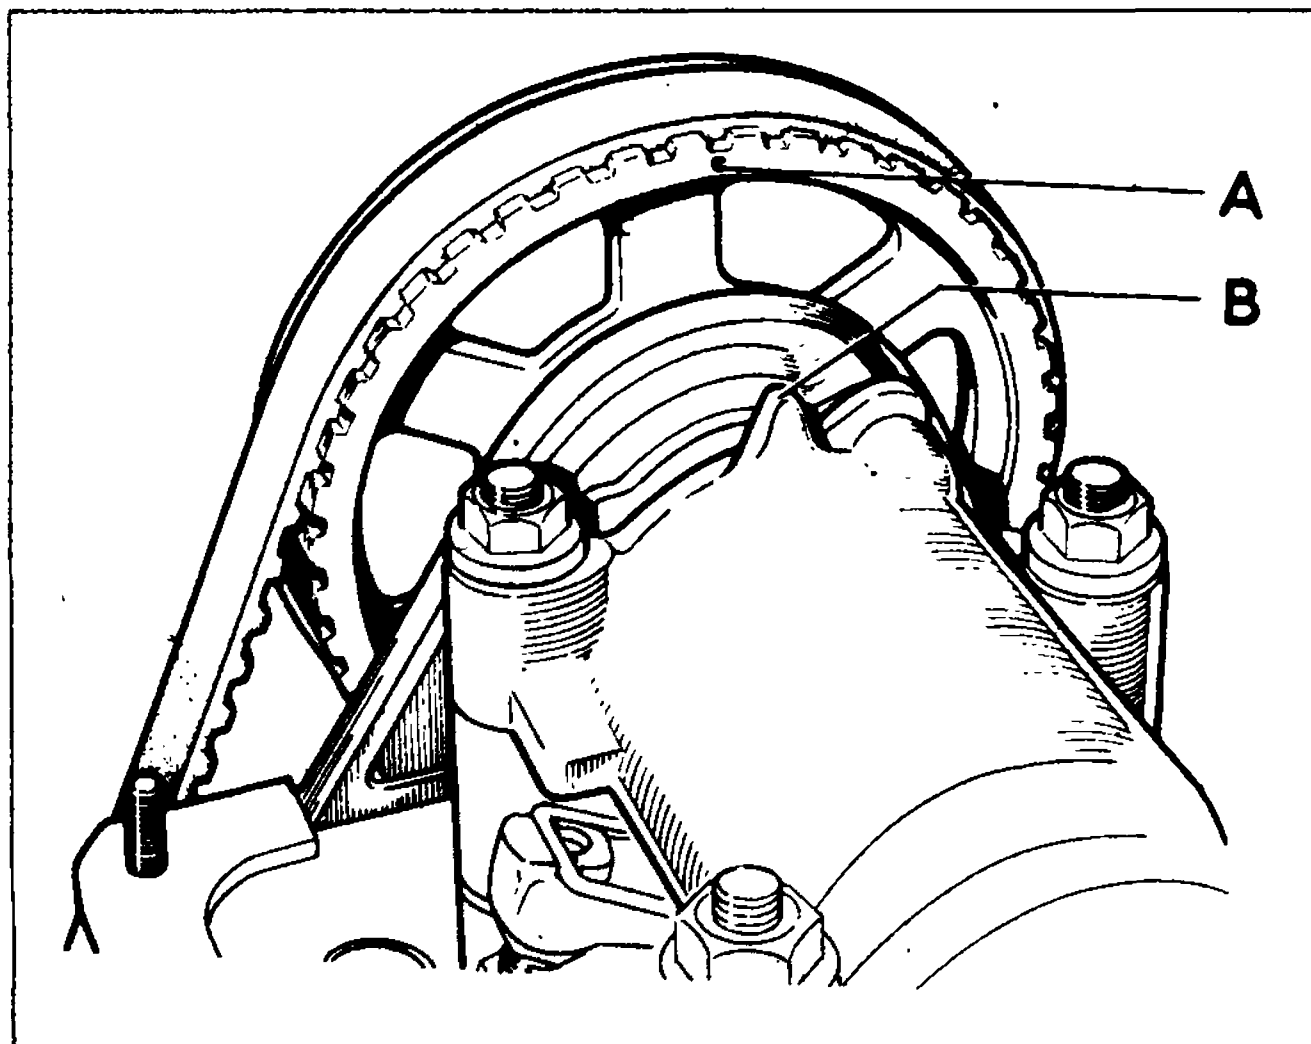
Проверка совпадения установочной метки на шкиве распределительного вала с меткой на корпусе подшипников: А-метка на шкиве; В-метка на корпусе подшипников
